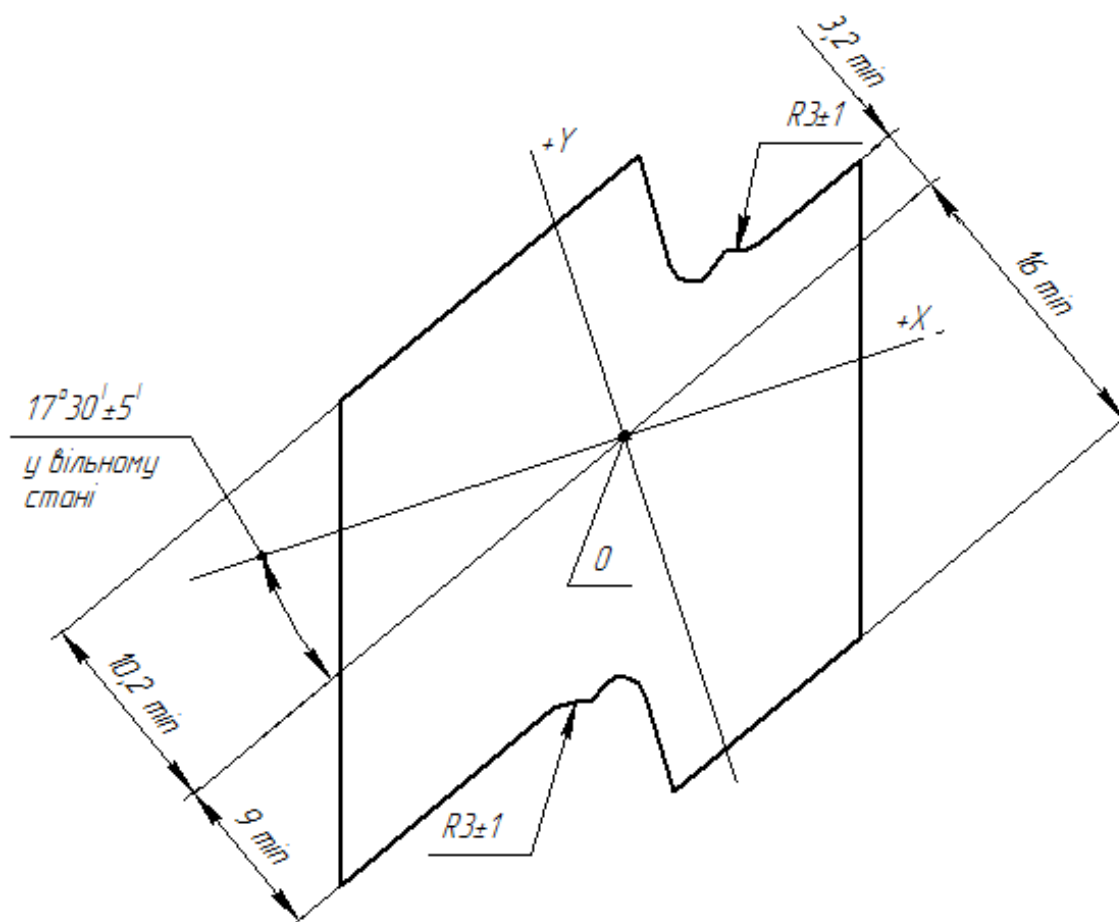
Бандажна полка робочої лопатки ТСТ підготовленої під наплавлення.
